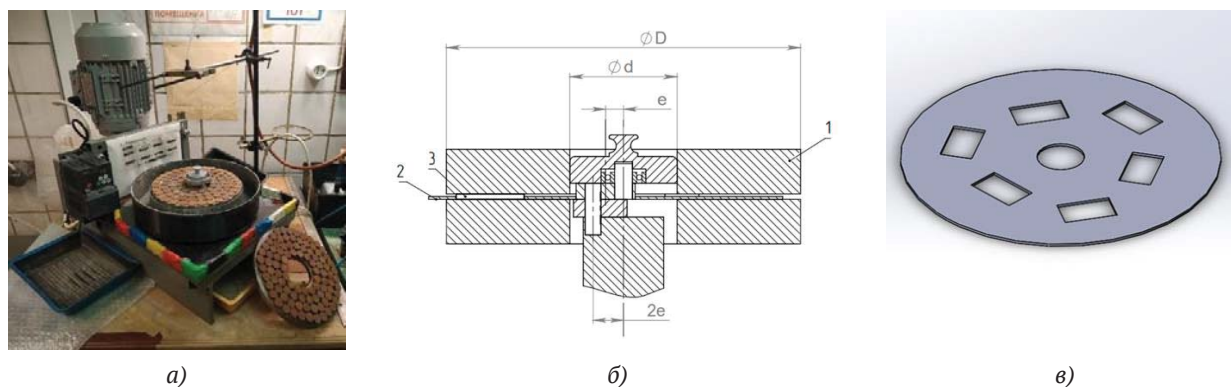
Внешний вид (а), схема (б) и конструкция сепаратора (в) настольного станка для групповой двухсторонней доводки эксцентрикового типа
